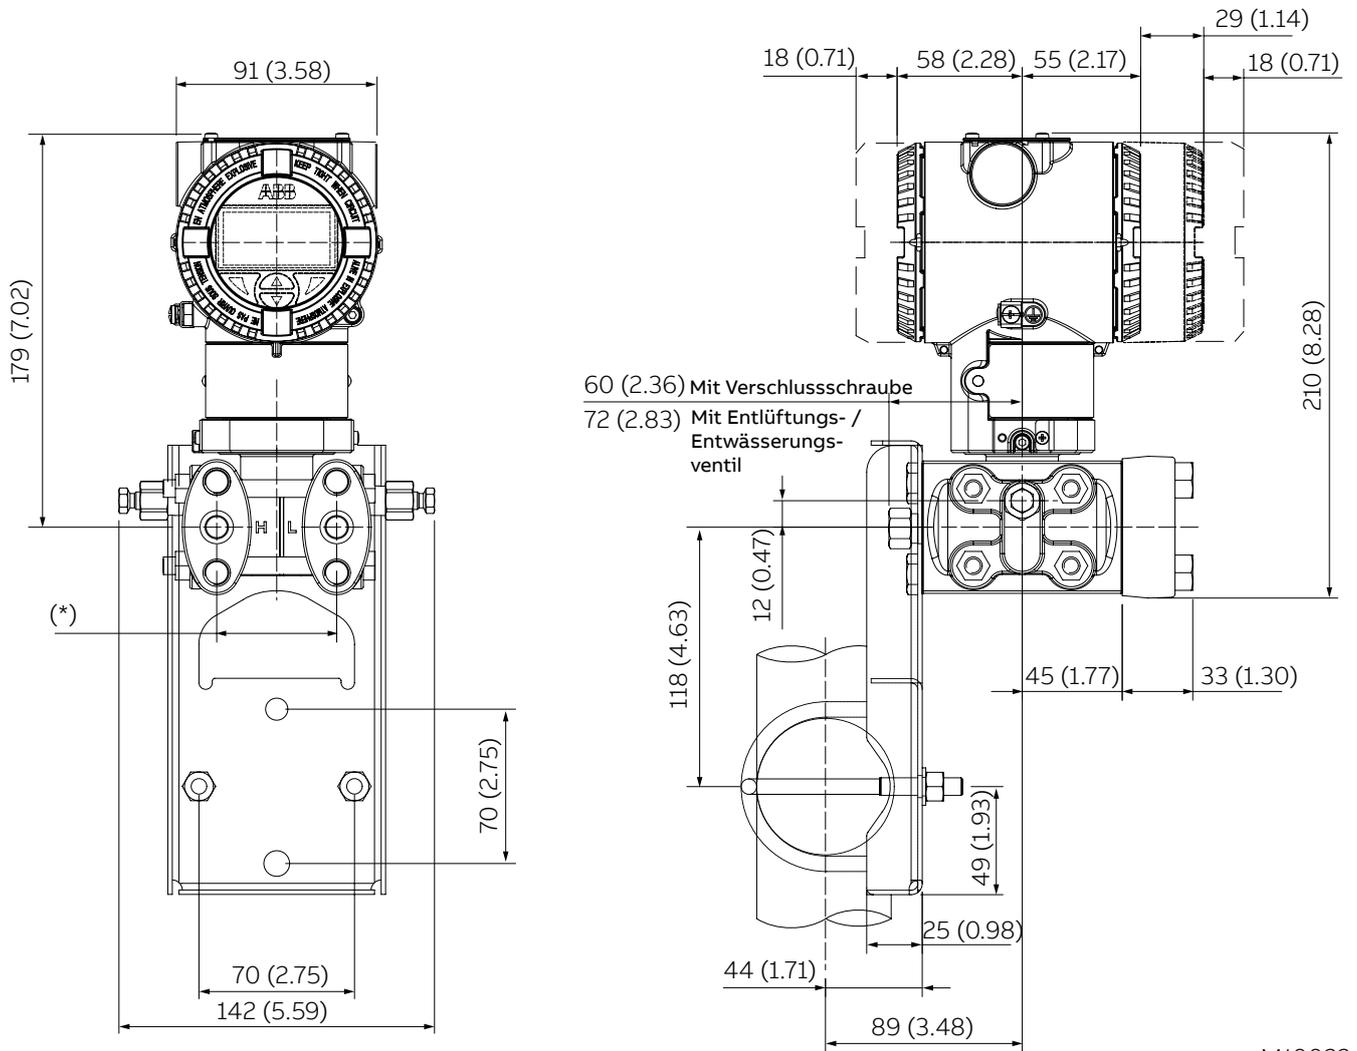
Messumformer mit DIN-Aluminiumgehäuse – horizontale Flansche mit Befestigungshalterung zur vertikalen oder horizontalen Montage an 60 mm (2 inch) Rohr
